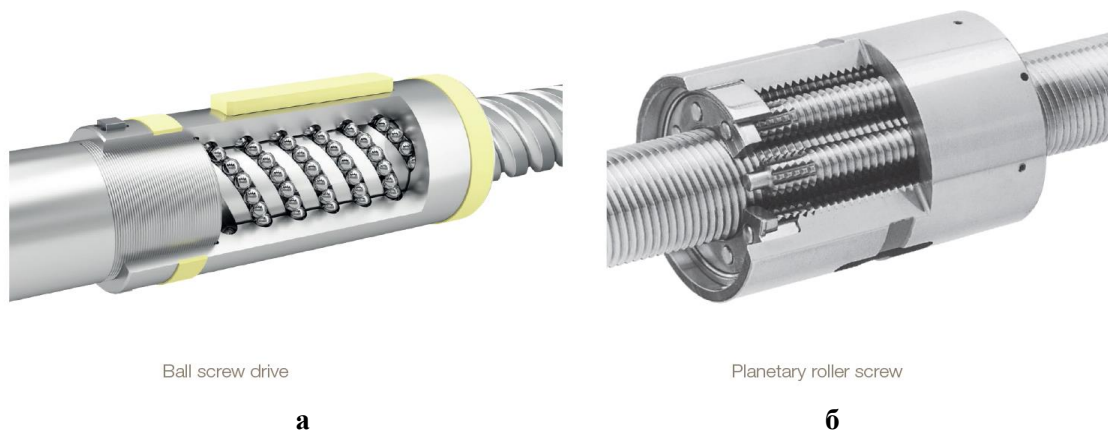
Механічні перетворювачі обертального руху у лінійний рух: а – кульково-гвинтова передача; б – планетарна роликowo-гвинтова передача [28]
